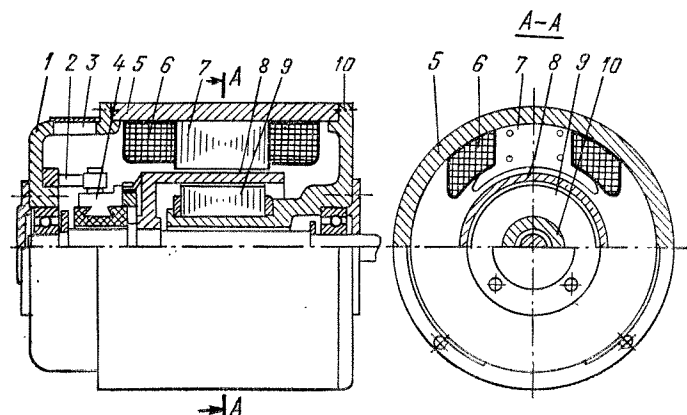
Исполнительный двигатель постоянного тока с полым немагнитным якорем
